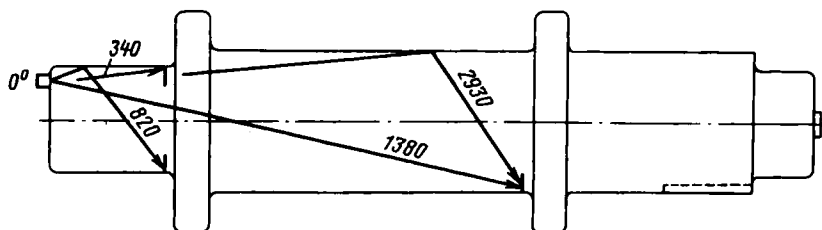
Схемы и зоны контроля прямым искателем со стороны левого торца главного приводного вала эскалатора Н-40М
